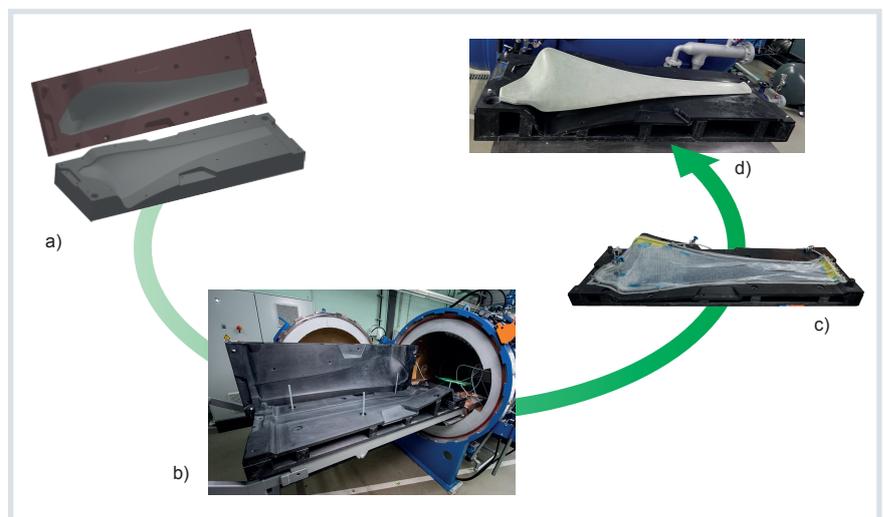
Entwicklungsprozess des Formwerkzeugs für die Rotorblattherstellung. a) CAD-Modell des Formwerkzeugs; b) gedrucktes Werkzeug; c) Infusion einer Rotorblatthälfte; d) Rotorblatt nach der Verklebung beider Schalenhälften Quelle: BTU; Grafik: © Hanser
